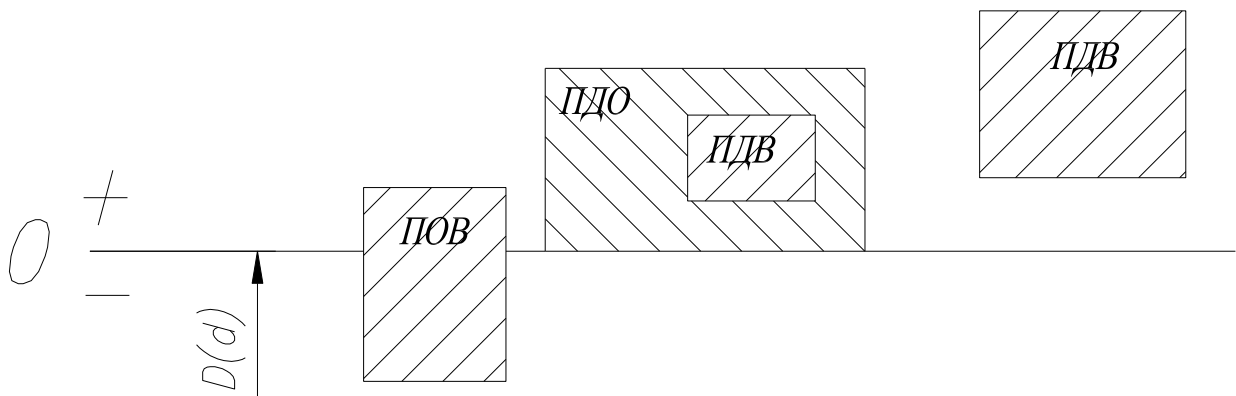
6. Схема розташування полів допусків перехідного з'єднання
